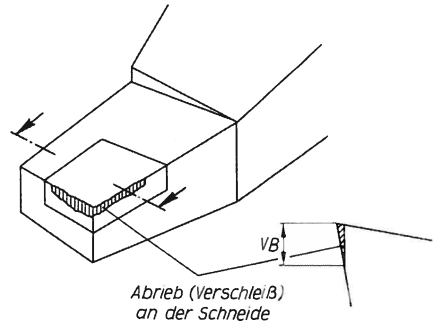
Werkzeugverschleiß beim Zerspanen von Aluminiumwerkstoffen
